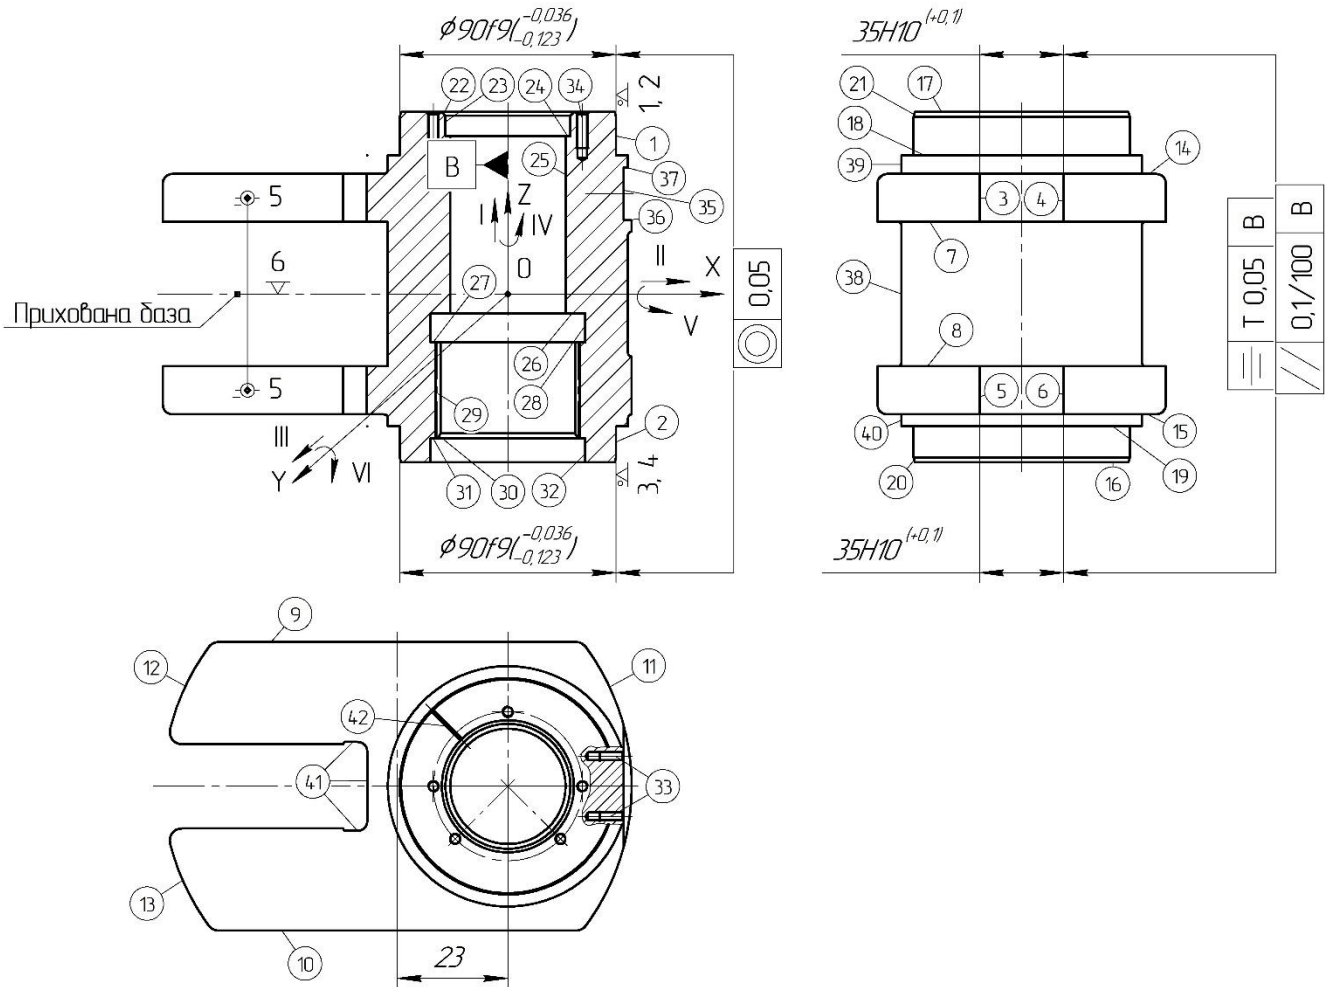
Схема базування важеля у механізмі повороту
